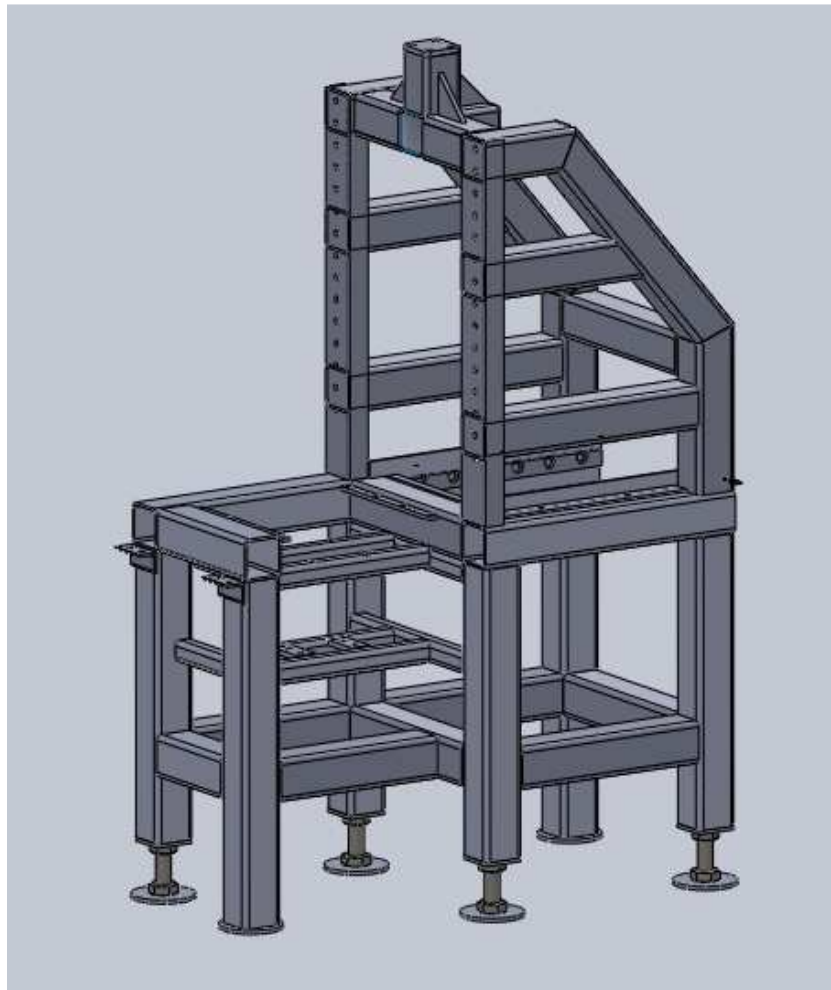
Conjunto soldado de la estructura del cabezal
